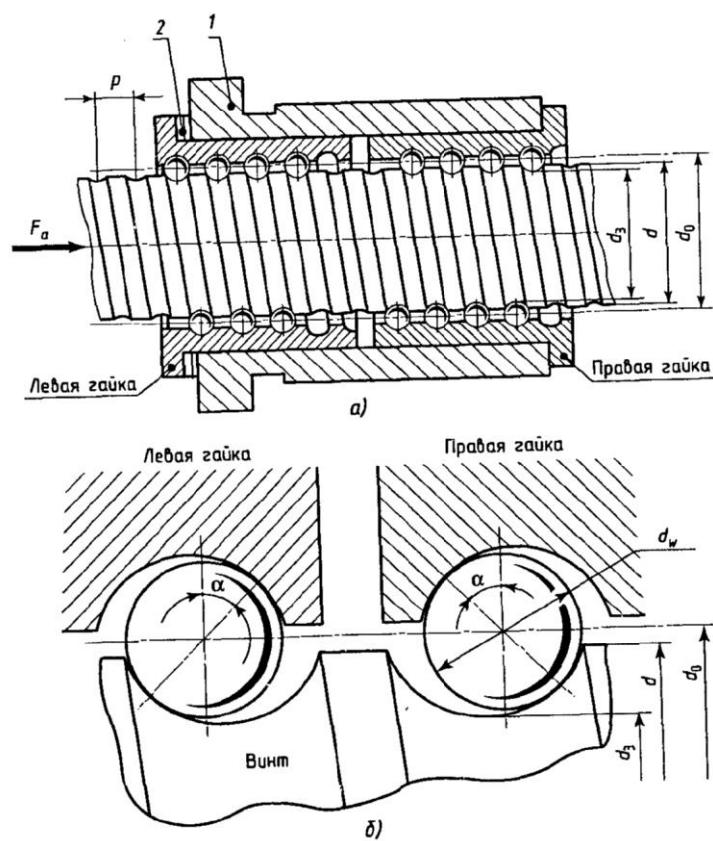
Расчетная схема шариковой передачи с двумя гайками: 1- корпус, 2- регулировочные прокладки
